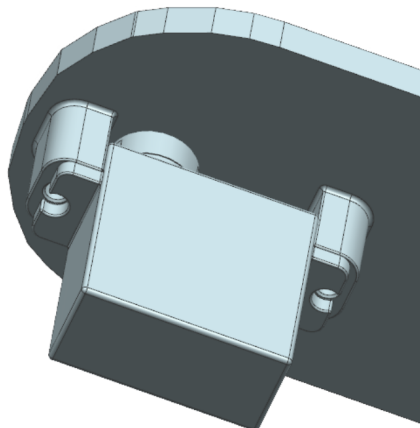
Diseño definitivo soporte servo horizontal; Fuente propia
